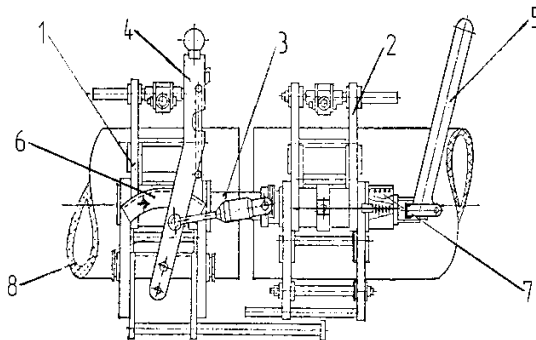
Сварочная установка с рычажным приводом: 1, 2 - зажимы; 3 - направляющие; 4 - приводной рычаг; 5 - упорный рычаг; 6 - храповый тормоз; 7 - динамометр со стрелочным указателем; 8 - свариваемые трубы
